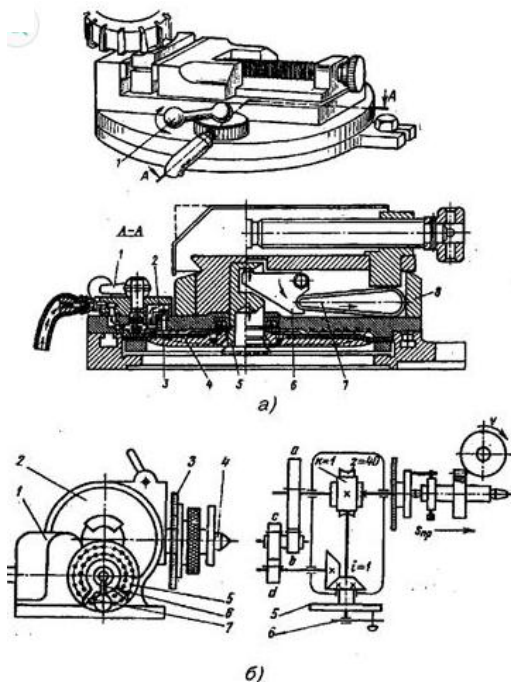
Пристрої для закріплення заготовок на фрезерних верстатах:
